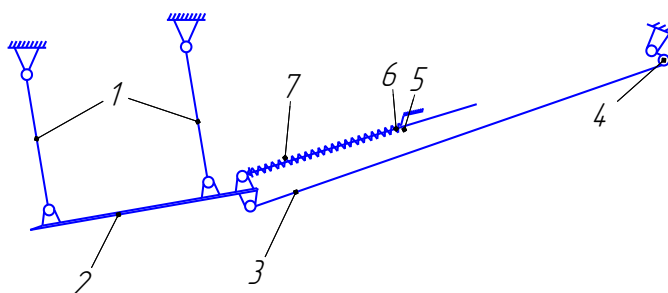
Схема підкопувального робочого органа корнеклубнезбиральної машини: 1 – підвіски; 2 – леміш; 3 – гнучка тяга; 4 – кривошип; 5 – шток; 6 – опора; 7 – пружина
